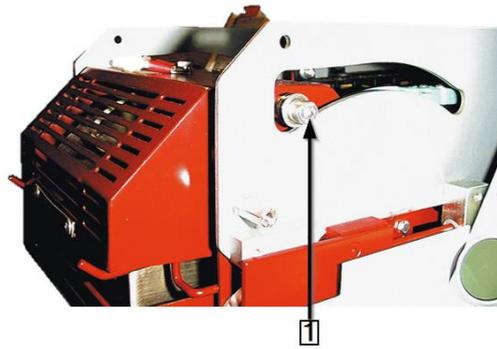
Tornillo de rodamiento del elemento calefactor
